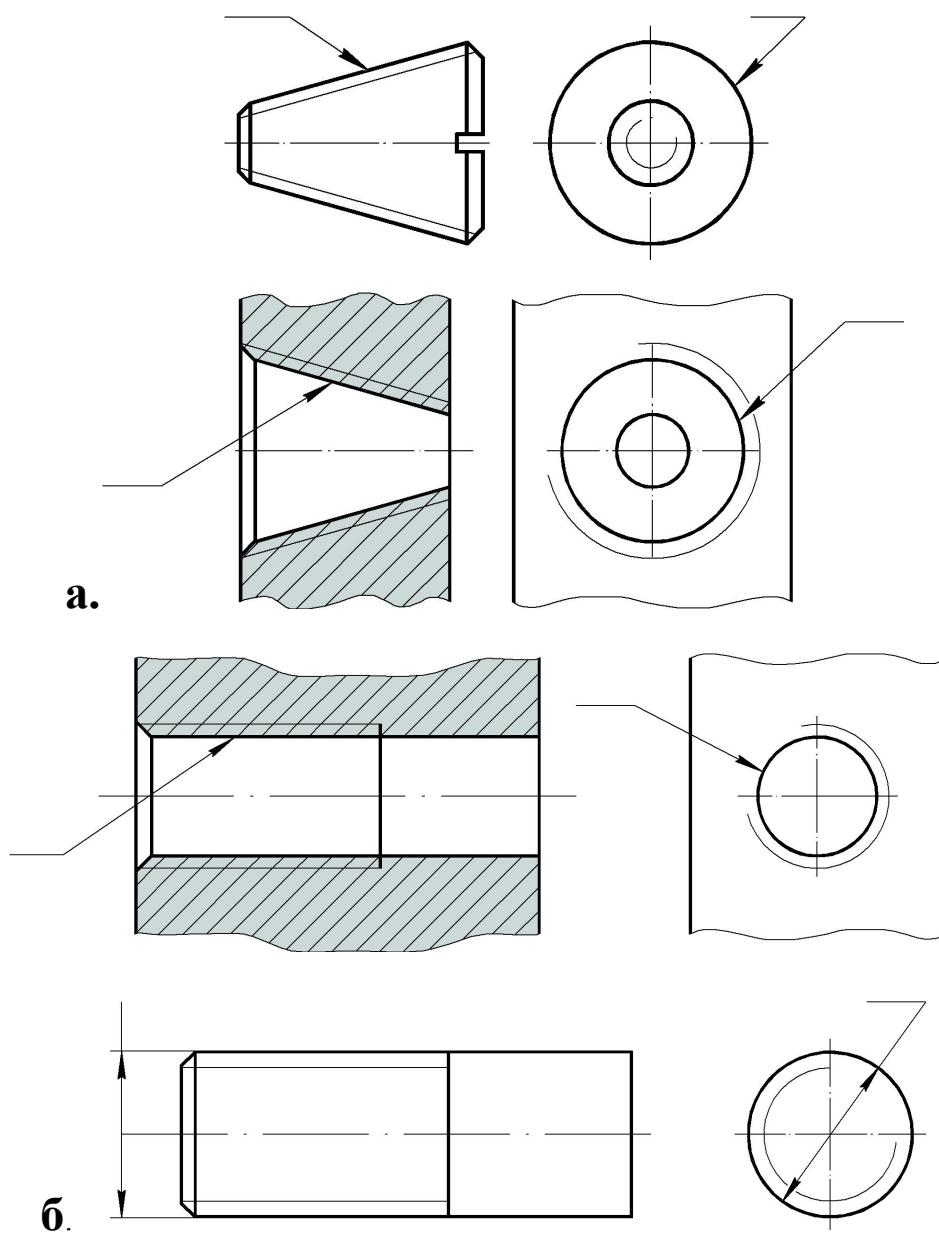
Обозначение на чертежах резьб: а.- конической наружной, конической внутренней и трубной цилиндрической; б- определяемых наружным диаметром резьбы
